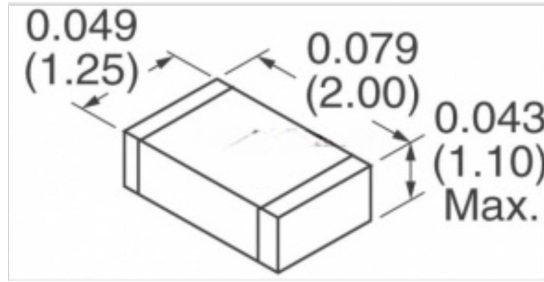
Габаритні розміри резистора RC0805FR
